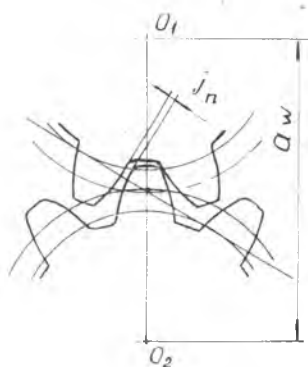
Схема образования бокового зазора в зацеплении зубчатых колес
